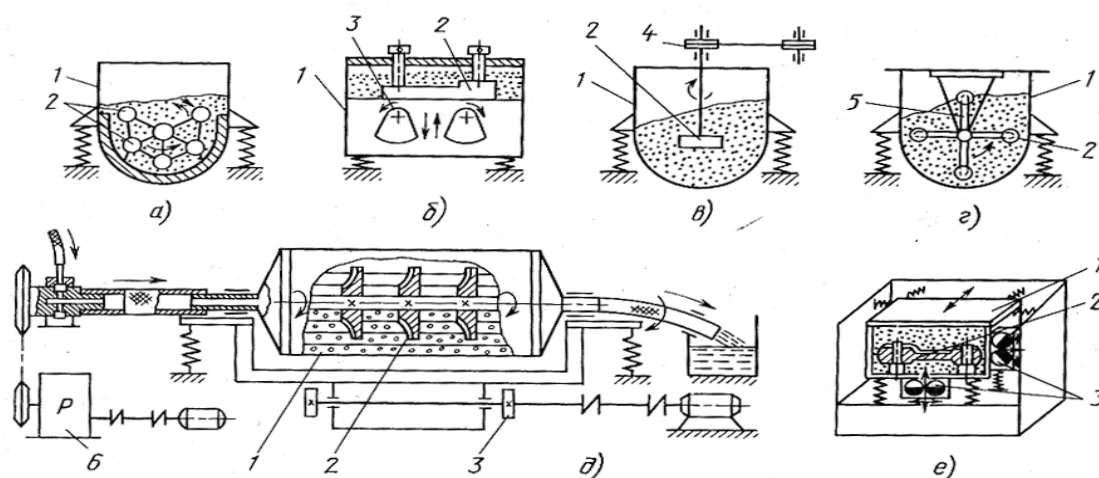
Схема виброударной обработки деталей с закреплением в контейнере:
